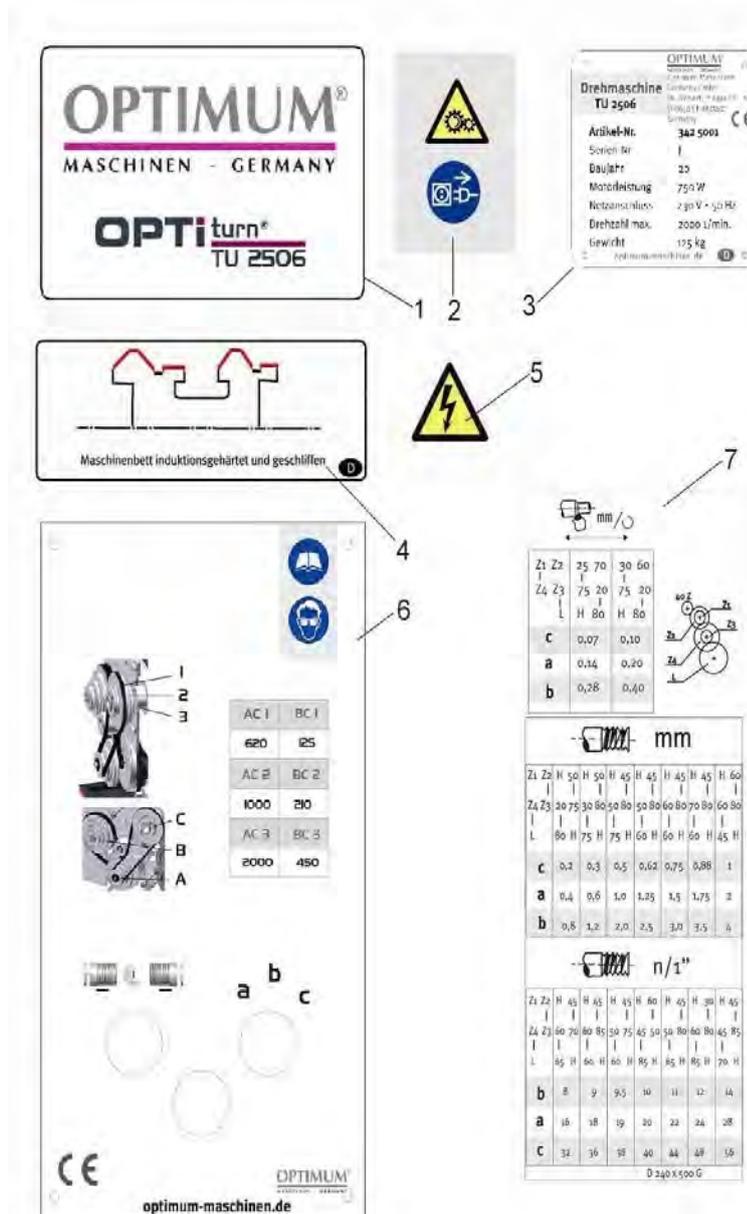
Maschinenschilder - Etiquetas de máquina
